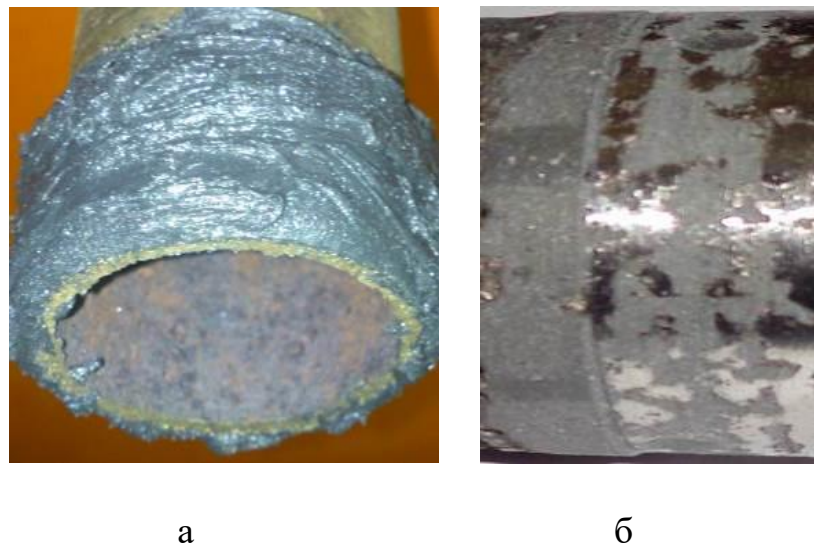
Нанесений на поверхню валу ПМ (а) іпроточена поверхня (б)
